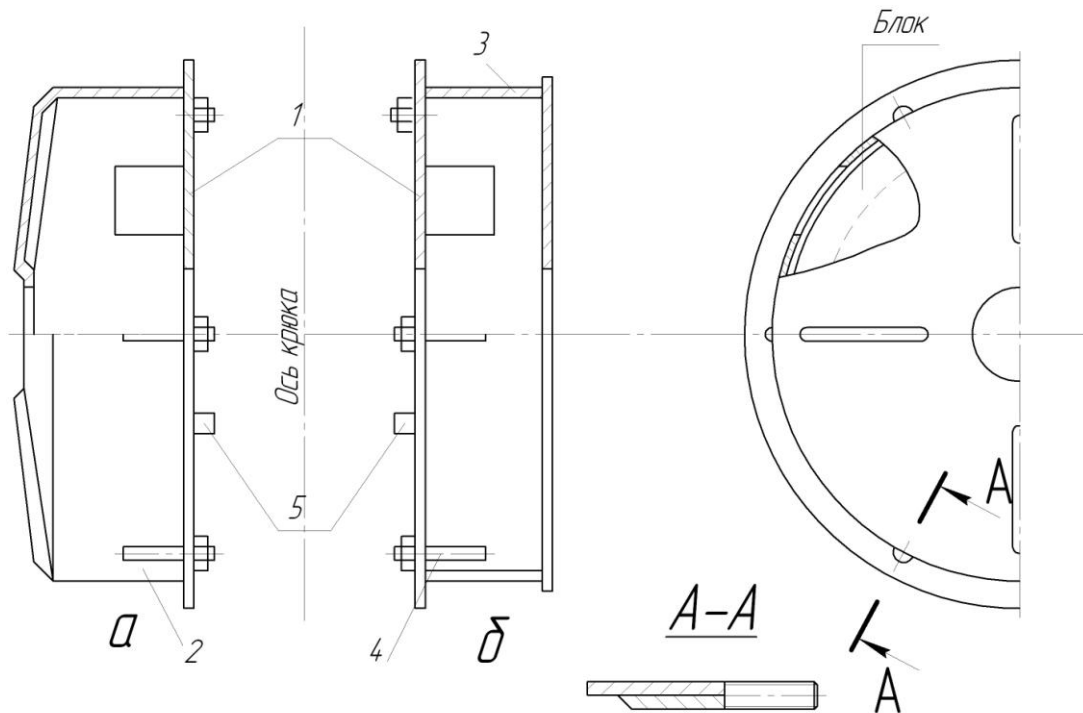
Закритий кожух укороченої підвіски: штапований (а), зварений(б)
